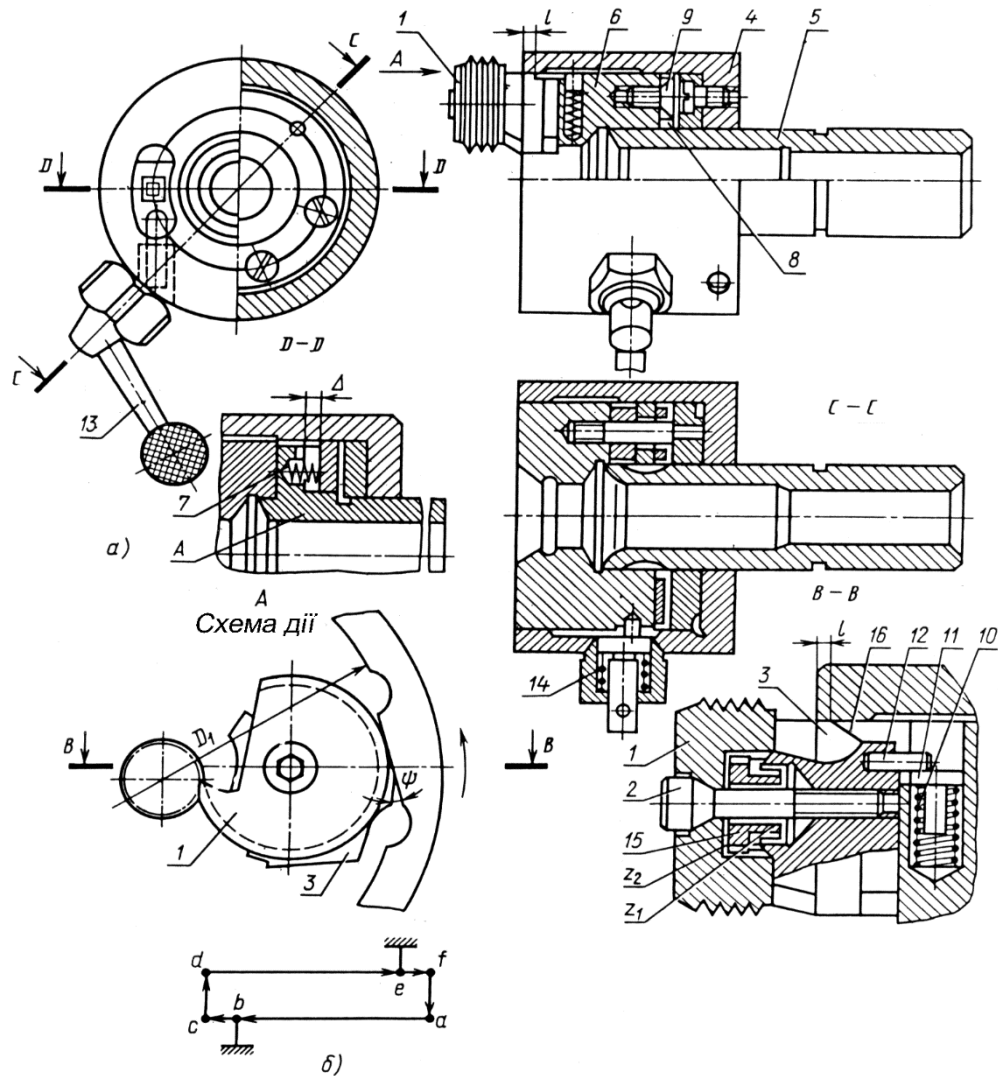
Конструкція (а) та принципи роботи (б) різьбонарізної головки з круглими гребінками: 1 – гребінки; 2 – гвинти; 3 – кулачки; 4 – корпус; 5 – хвостовик; 6 – плашкодержач; 7 – пружини; 8 – кільце; 9 – гвинти; 10 – пружини; 11 – штифти; 12 – шпильки; 13 – ручка; 14 – пружина; 15 – зірочка; 16 – скіс кулачків. Накатування є найбільш продуктивним способом утворення різьби без зняття стружки методом пластичного деформування. Переваги цього методу перед різьбонарізанням:
